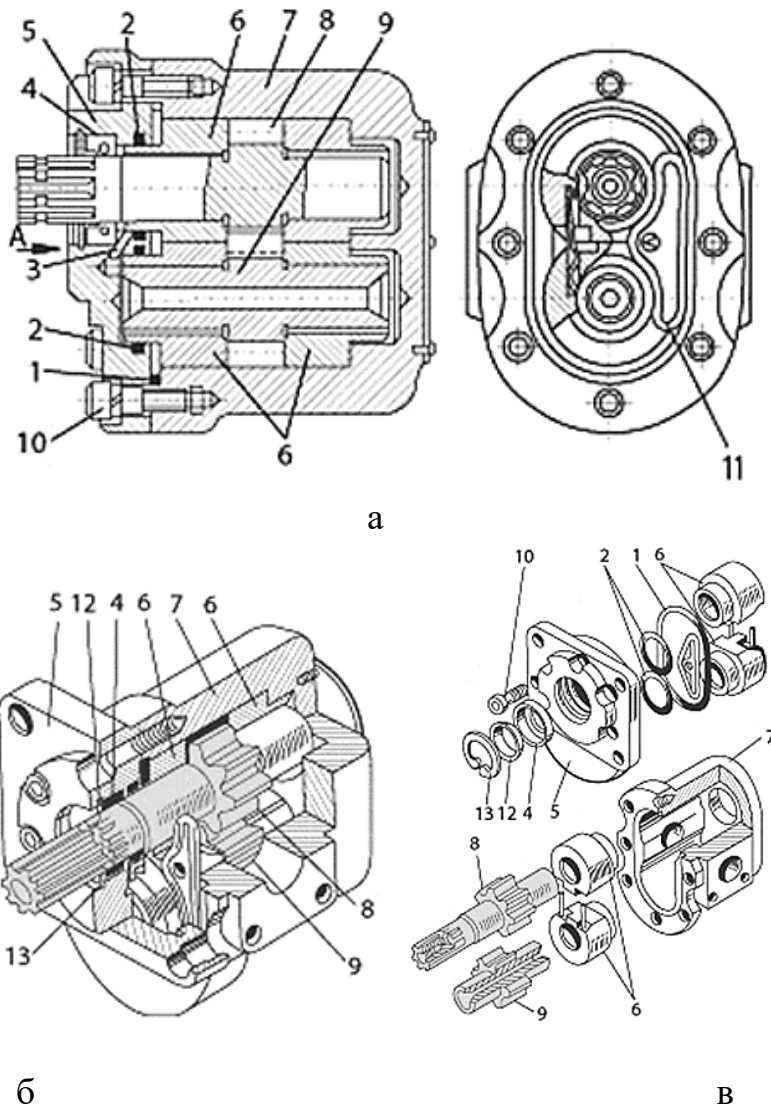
Односекційний шестеренний насос: а і б – насос у розрізі, в – основні деталі насоса; 1, 2 – кільця; 3 – отвір; 4 – ущільнення; 5 – кришка; 6 – втулки; 7 – корпус насоса; 8, 9 – шестерні; 10 – болти; 11 – пластину; 12 – кільця.
